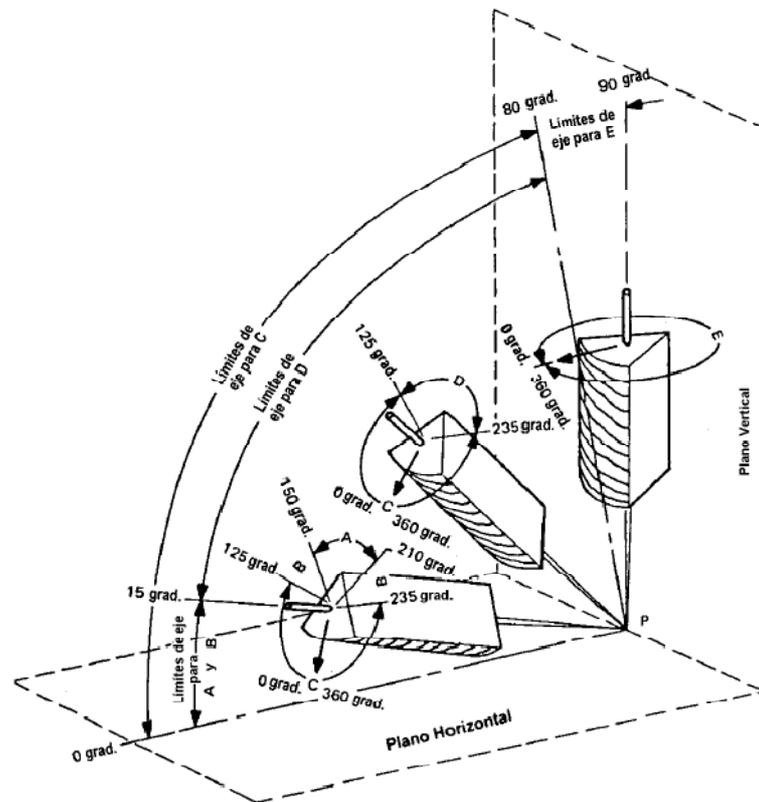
Posiciones para Soldadura a Filete
